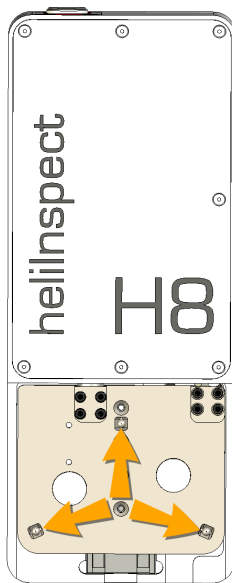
Position der V-Nuten am Gehäusekörper des heliInspect™ H8
